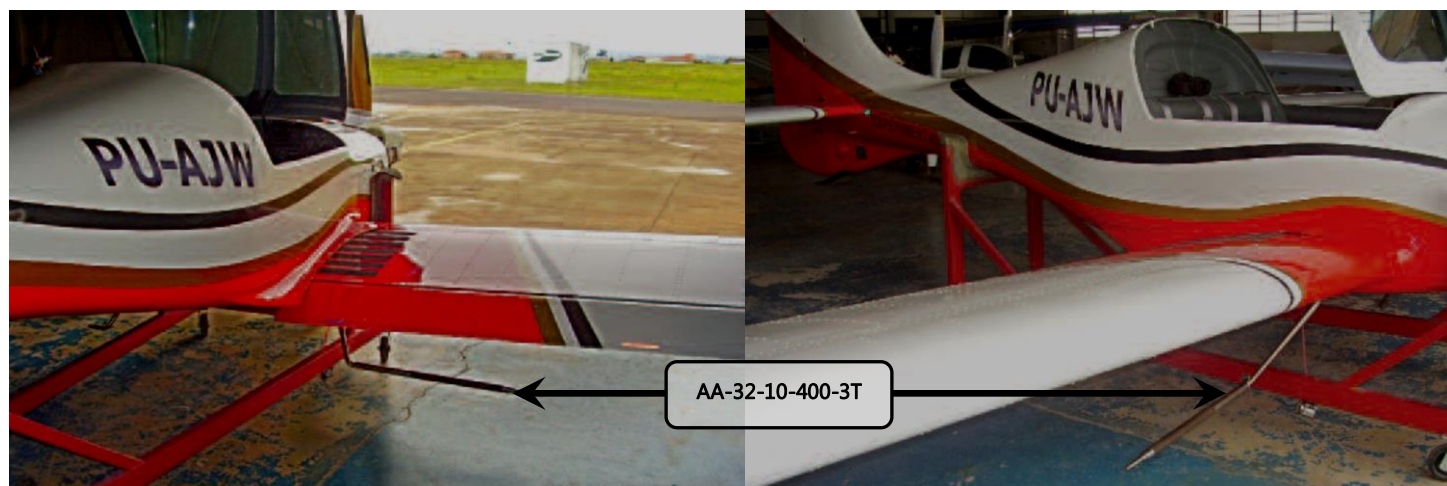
Instalação da ferramenta AA-32-10-400-3T
